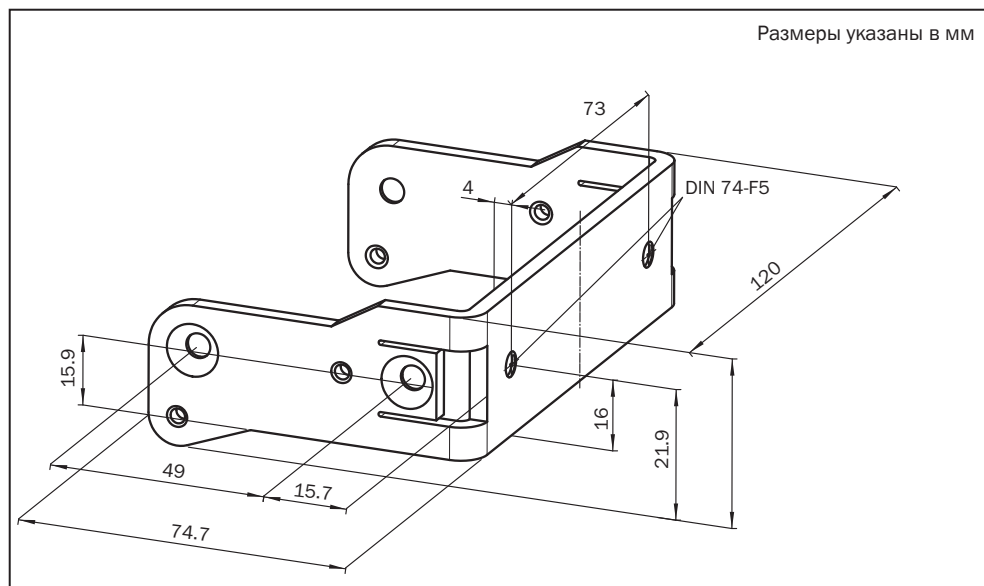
Размерный чертёж монтажного комплекта №1а (Артикул 2034324)
